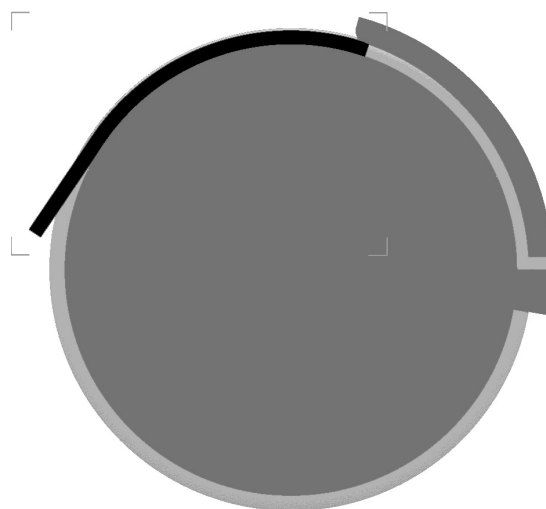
Эскиз первоначального положения заготовки в канале прессования
